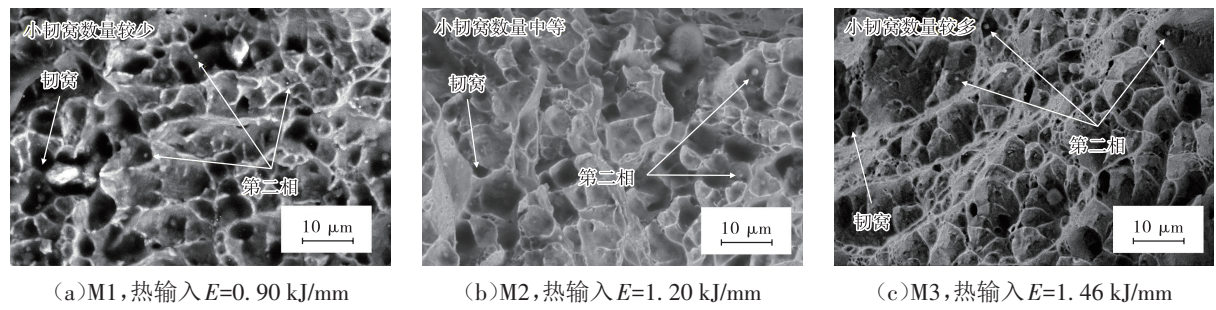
316LN-Mn 奥氏体不锈钢焊接接头断口形貌
